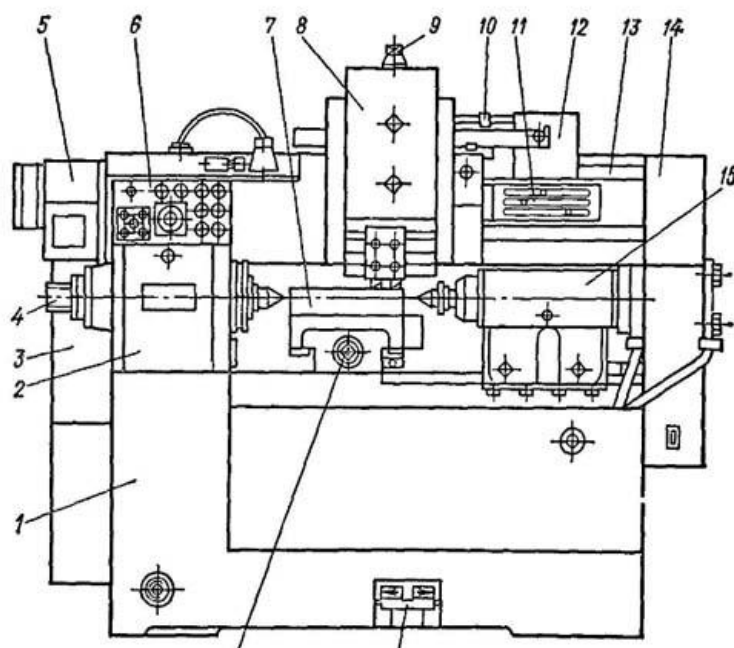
Основные узлы и исполнительные органы станка 1Н713: 1-станина полуавтомата, 2- передняя бабка, 3- кожух, 4- шпиндель, 5- коробка подачи, 6- пульт управления, 7- поперечный суппорт, 8-продольный суппорт, 9-квадратные рукоятки, 10 -передвижной упор, 11-командоаппарат, 12- копрная линейка, 13- верхняя станина, 14-электрошкаф, 15- задняя бабка, 16 -педаль пневмосистемы
